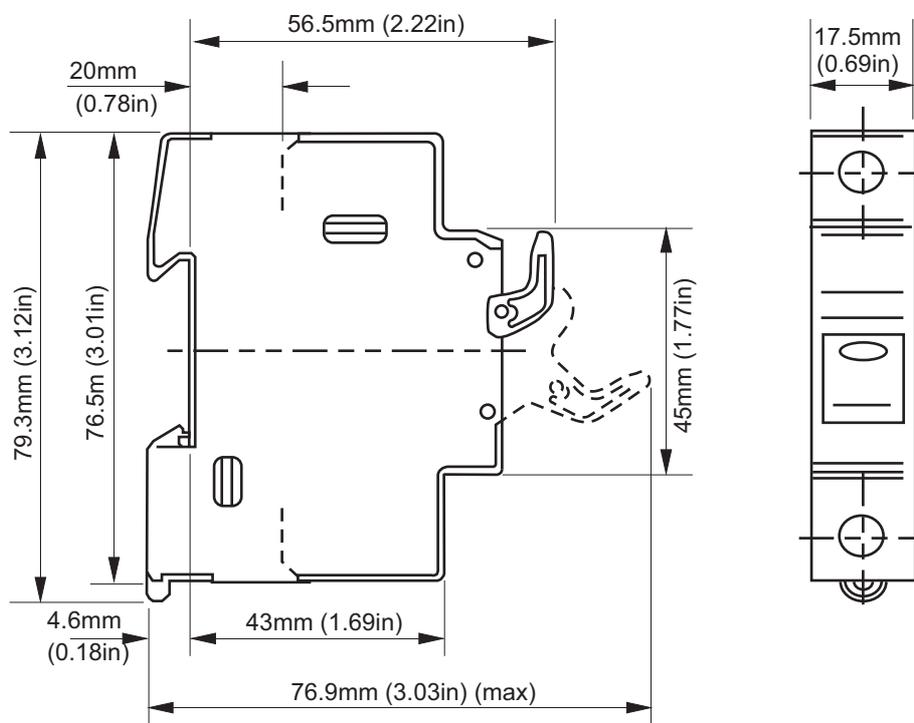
Dimensions du porte-fusible : CUS101 (10x38 mm)
